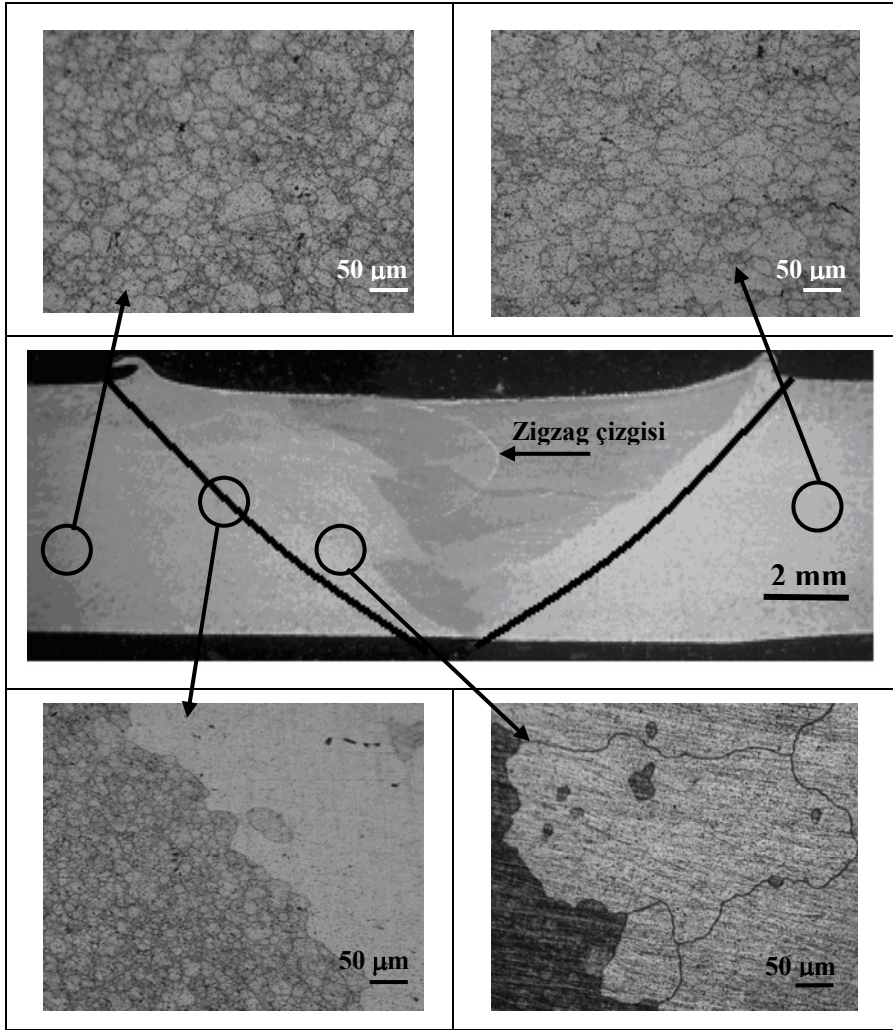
Kaynak bölgesinde zigzag oluşumu
